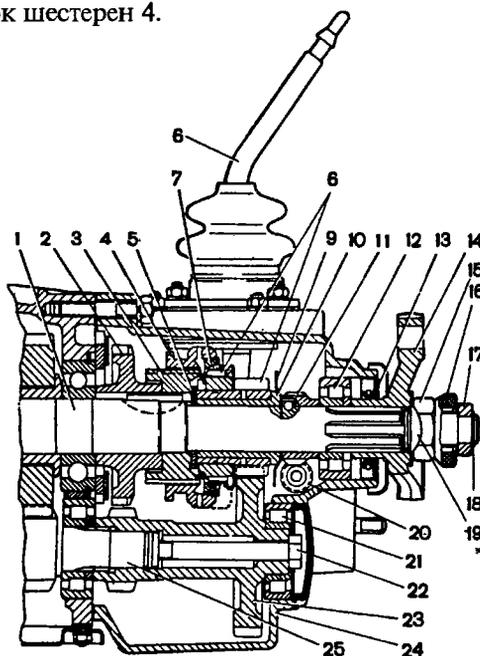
Задняя часть пятиступенчатой коробки передач: 1 - вторичный вал; 2 - ведомая шестерня заднего хода; 3 - ступица муфты синхронизатора V передачи; 4 - муфта синхронизатора; 5 - шайба; 6 - рычаг переключения передач; 7 - блокирующее кольцо синхронизатора; 8 - шестерня и зубчатый венец синхронизатора V передачи; 9 - маслоотражательная шайба; 10 - втулка шестерни V передачи; 11 - ведущая шестерня привода спидометра; 12 - задний подшипник вторичного вала; 13 - сальник; 14 - фланец эластичной муфты; 15 - гайка; 16 - уплотнитель центрирующего кольца; 17 - центрирующее кольцо; 18 - стопорное кольцо; 19 - стопорная шайба; 20 - ведомая шестерня привода спидометра; 21 - подшипник блока шестерен; 22 - болт крепления блока шестерен; 23 - блок шестерен V передачи и заднего хода; 24 - задняя крышка коробки передач; 25 - промежуточный вал
